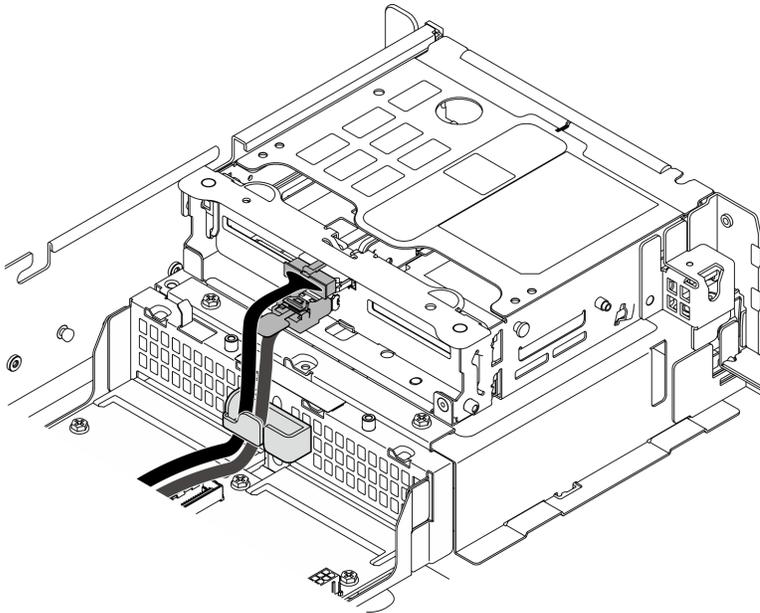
Disposición de los cables de la placa posterior de la unidad frontal
